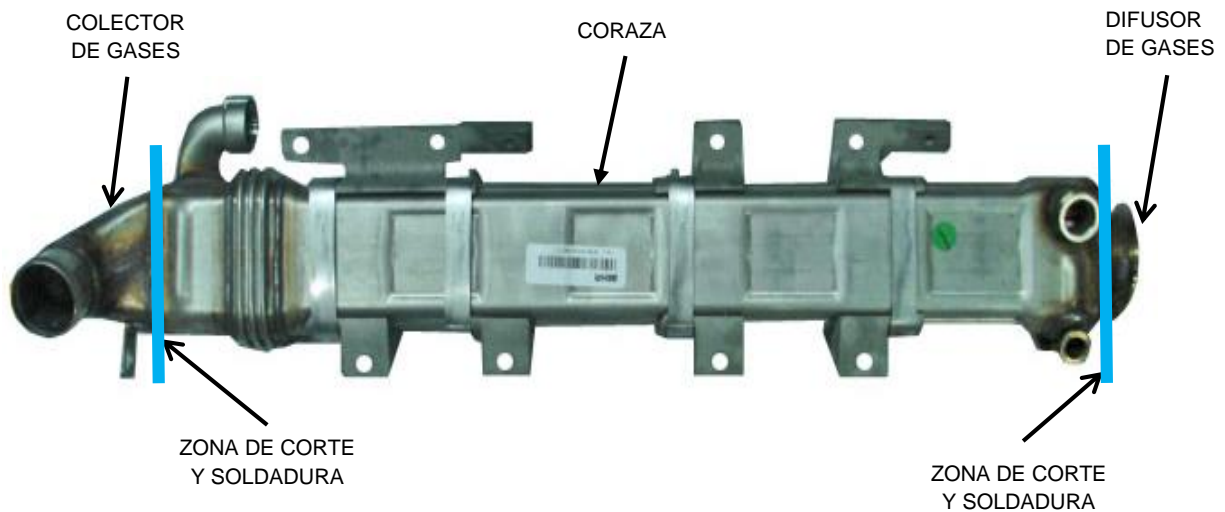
Zonas de corte y soldadura en intercambiador.
